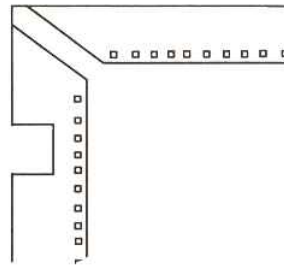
Die umgefalteten Laschen der Vorderseite sind mit 'Schweißpunkten' an der Rückseite befestigt.
